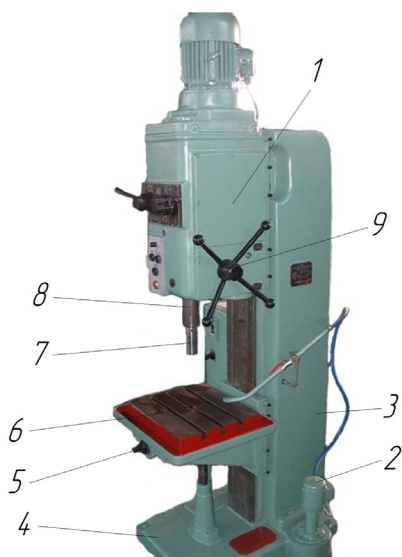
Вертикально-сверлильный станок модели 2Н135
